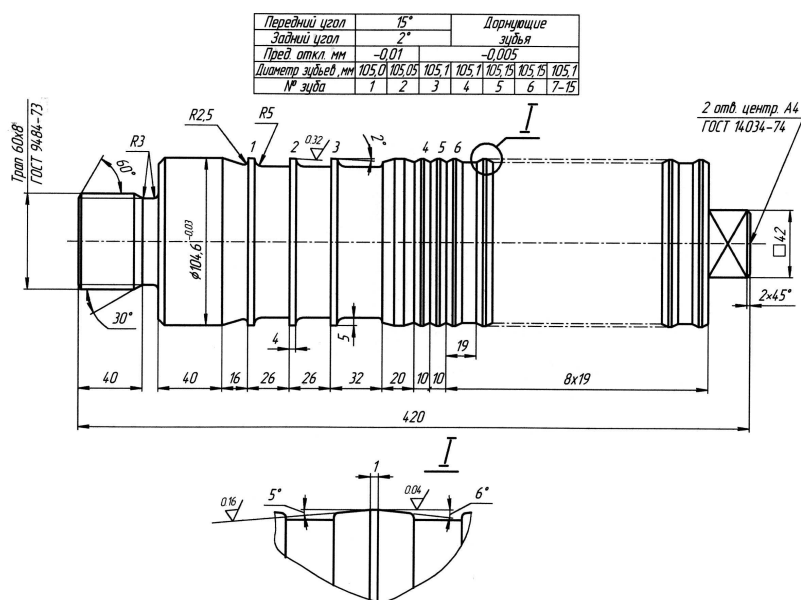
Вид прошивки пиноли для вихрефрезерования методом винтовой интерполяции [2]
